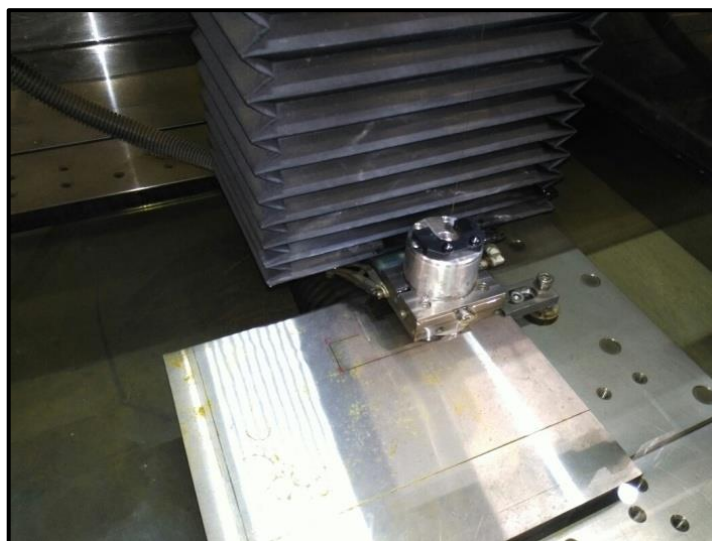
, drátová řezačka FANUC ROBOCUT α600 IA [8]
